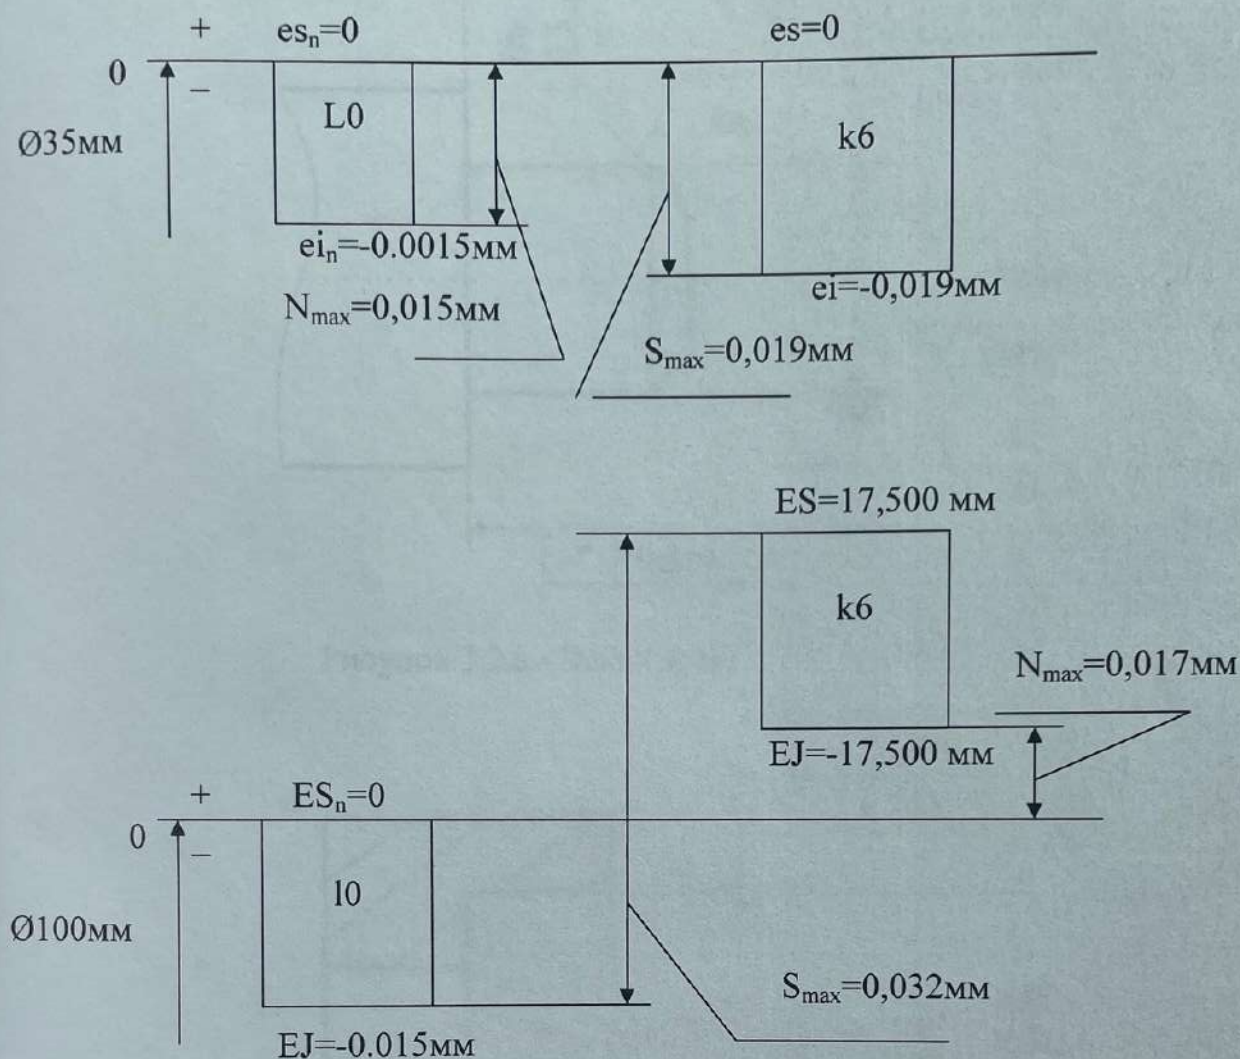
Схема расположения полей допусков для деталей подшипникового узла.
